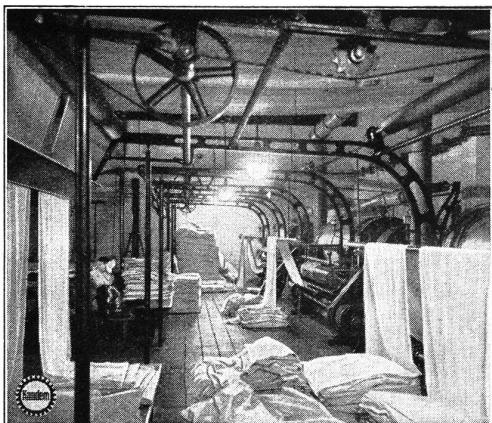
Rauhmaschinenbeleuchtung durch niedrig hängende Kandem-Leuchten für vorwiegend direktes Licht.
